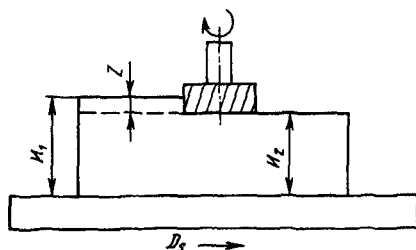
Связь размеров заготовки I_1 , изделия I_2 и припуска Z
